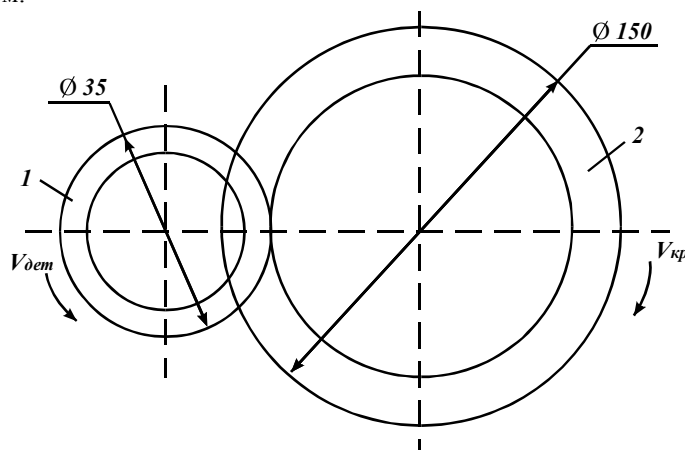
Схема шлифования торца вращающегося кольца торцом алмазного круга: 1- обрабатываемое кольцо, 2- алмазный круг.
